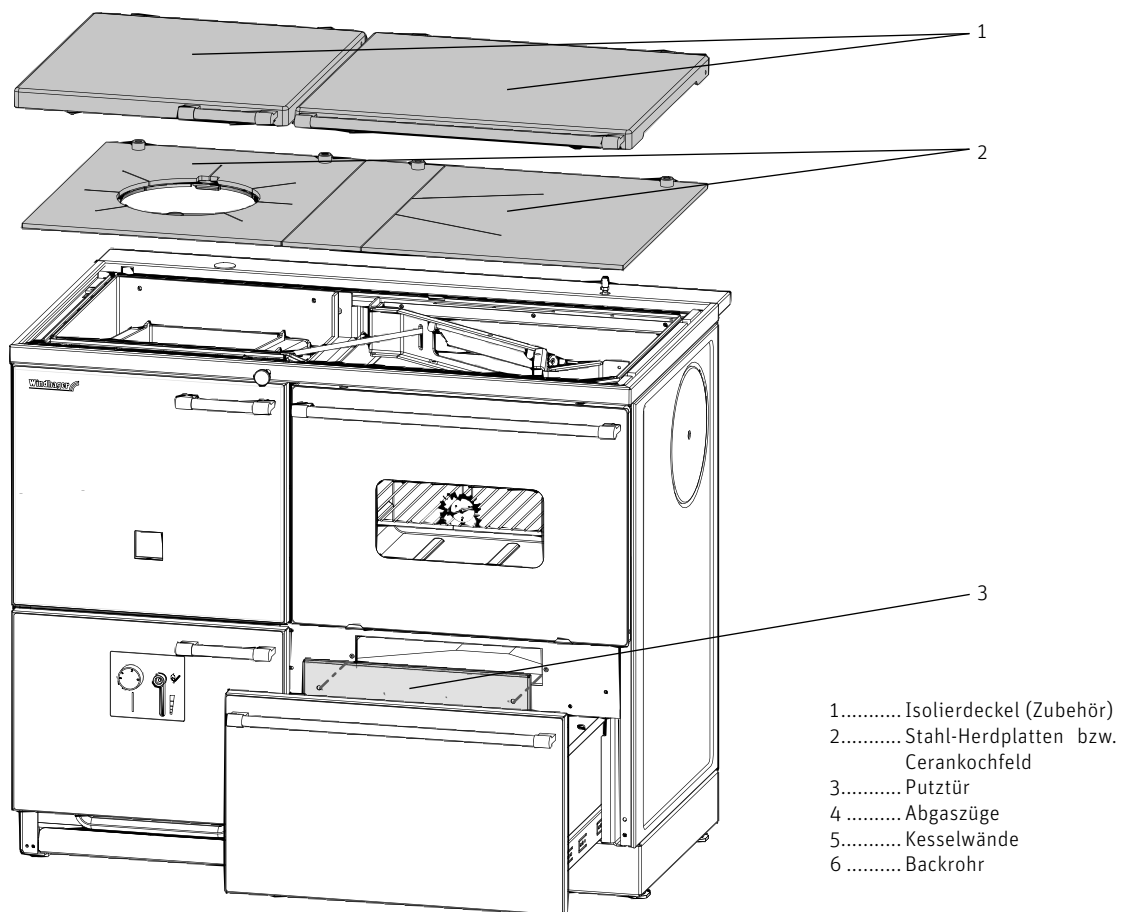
Isolierdeckel und Stahl-Herdplatte abnehmen, reinigen und Putztür unter Backrohr öffnen
